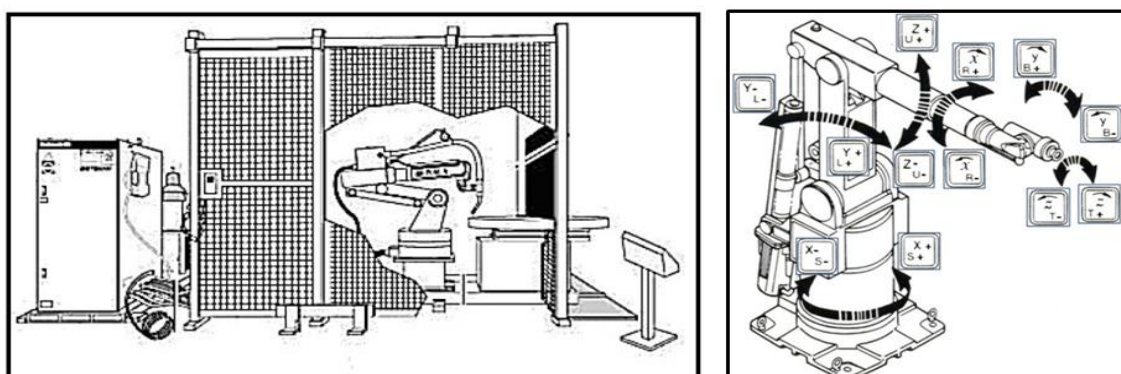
Esquema da célula de soldadura robotizada e dos seis movimentos do robot.
